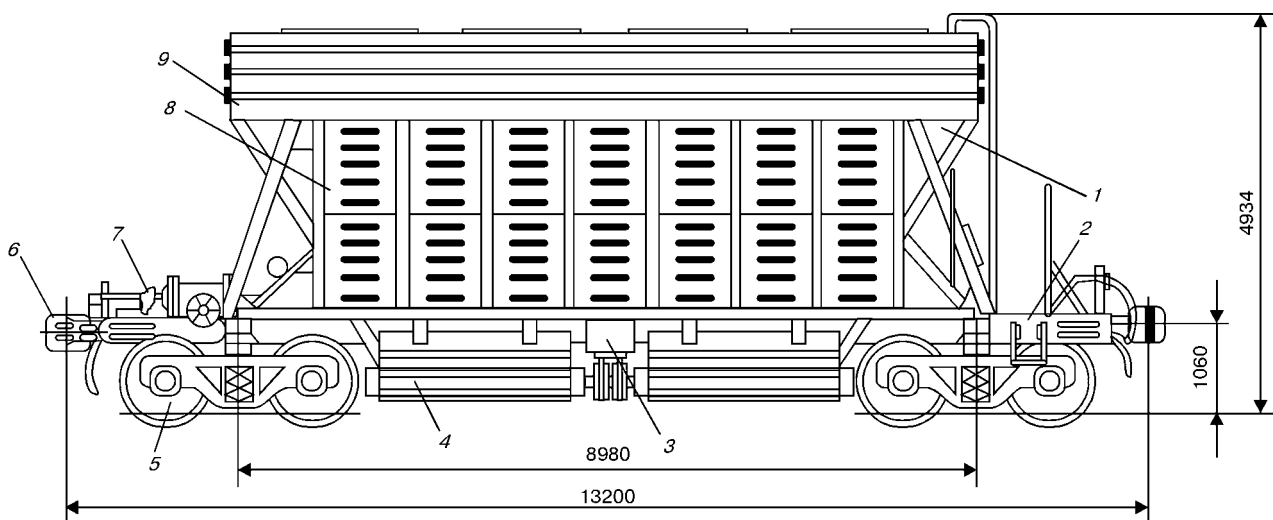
Вагон-хоппер для минеральных удобрений (модель 19-923): 1 — кузов с бункерами; 2 — рама; 3 — механизм разгрузки; 4 — крышки разгрузочных люков; 5 — ходовая часть; 6 — автосцепное устройство; 7 — автоматический тормоз; 8 — стена боковая; 9 — крыша с загрузочными люками
